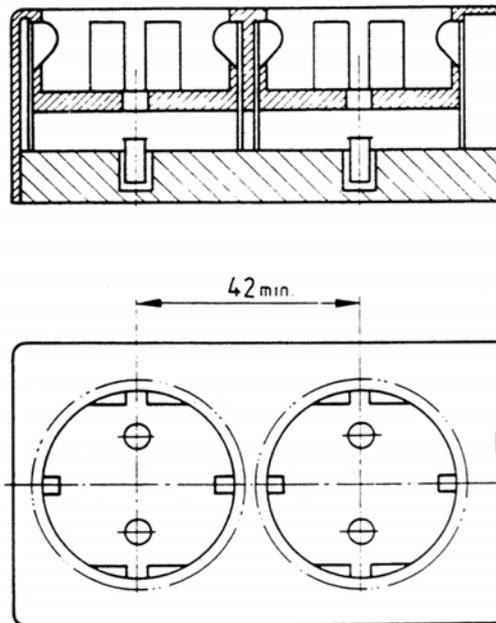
Mobile Mehrfach-Schutzkontaktsteckdose (MM)
